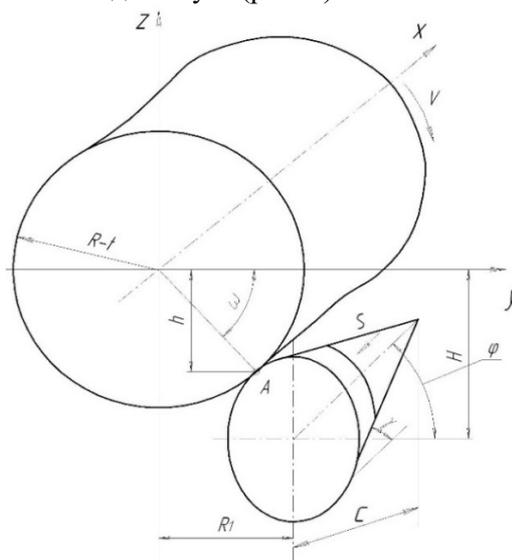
Расположение режущей чашки относительно обрабатываемой поверхности
